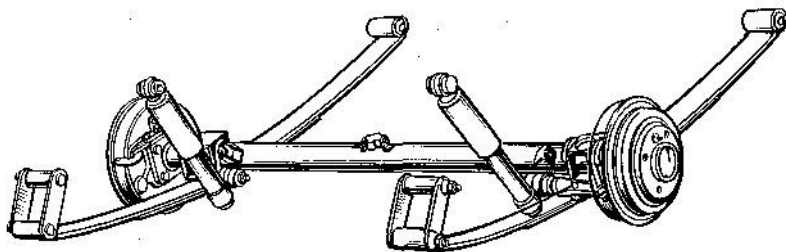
Задняя подвеска ведомых колес автомобиля «Фиат-панда» с широкими рессорами и установленными с выносом относительно оси колес наклоненными назад амортизаторами. Интересно, что проушина крепления амортизаторов к балке оси расположена сбоку от корпуса амортизатора. Усилия сжатия и отбоя, возникающие в амортизаторах при ходах колес, вызывают поворот балки оси
